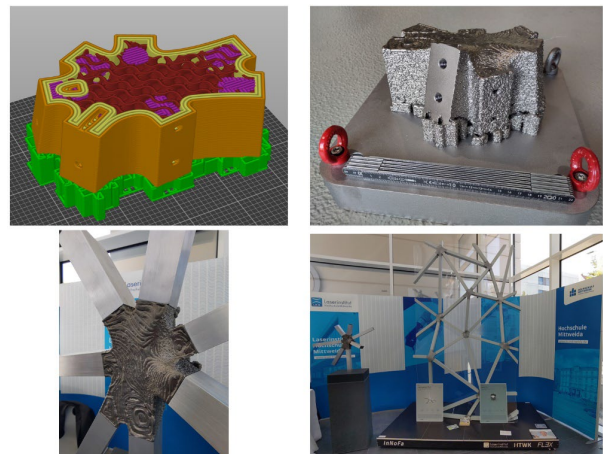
Additive Fertigung eines Fassadenknotens. *Oben links:* geslichtes 3D-Modell mit Blick ins Innere, 30% Infill. *Oben rechts:* Gefertigter Knoten auf der Bauplattform mit einseitig nachbearbeiteter Befestigungsfläche. Offset von 3 mm für Nachbearbeitung notwendig. *Unten links:* Fertiger Knoten mit Verbindungsstäben als Demonstrator. *Unten rechts:* Fassaden-Prototyp InNoFa mit individuell geformten, additiv gefertigten Knotenverbindungen.
